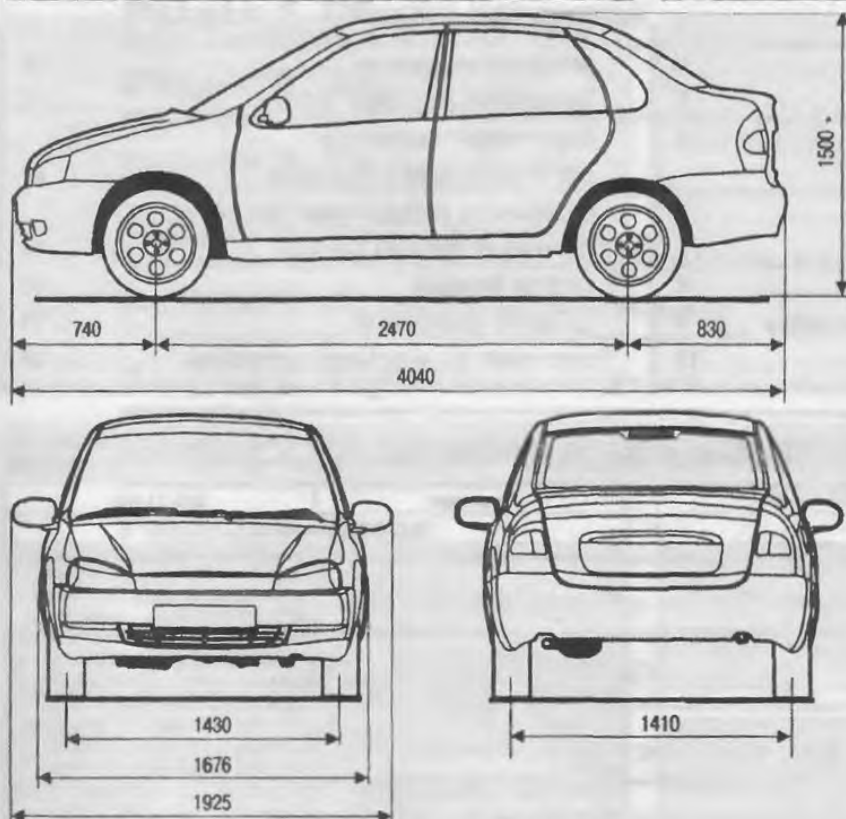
Габаритные размеры (справочные) автомобиля ВАЗ-11183
